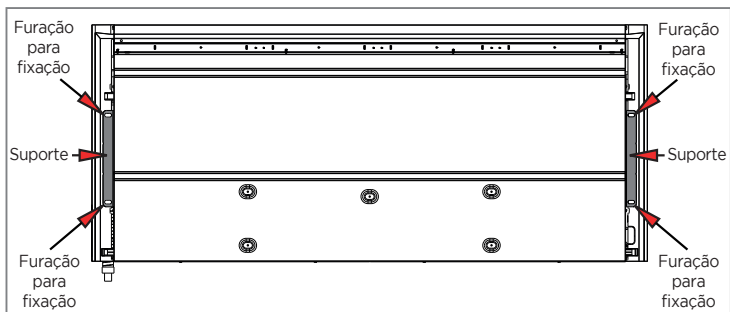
SUPORTES E FURAÇÃO PARA FIXAÇÃO
